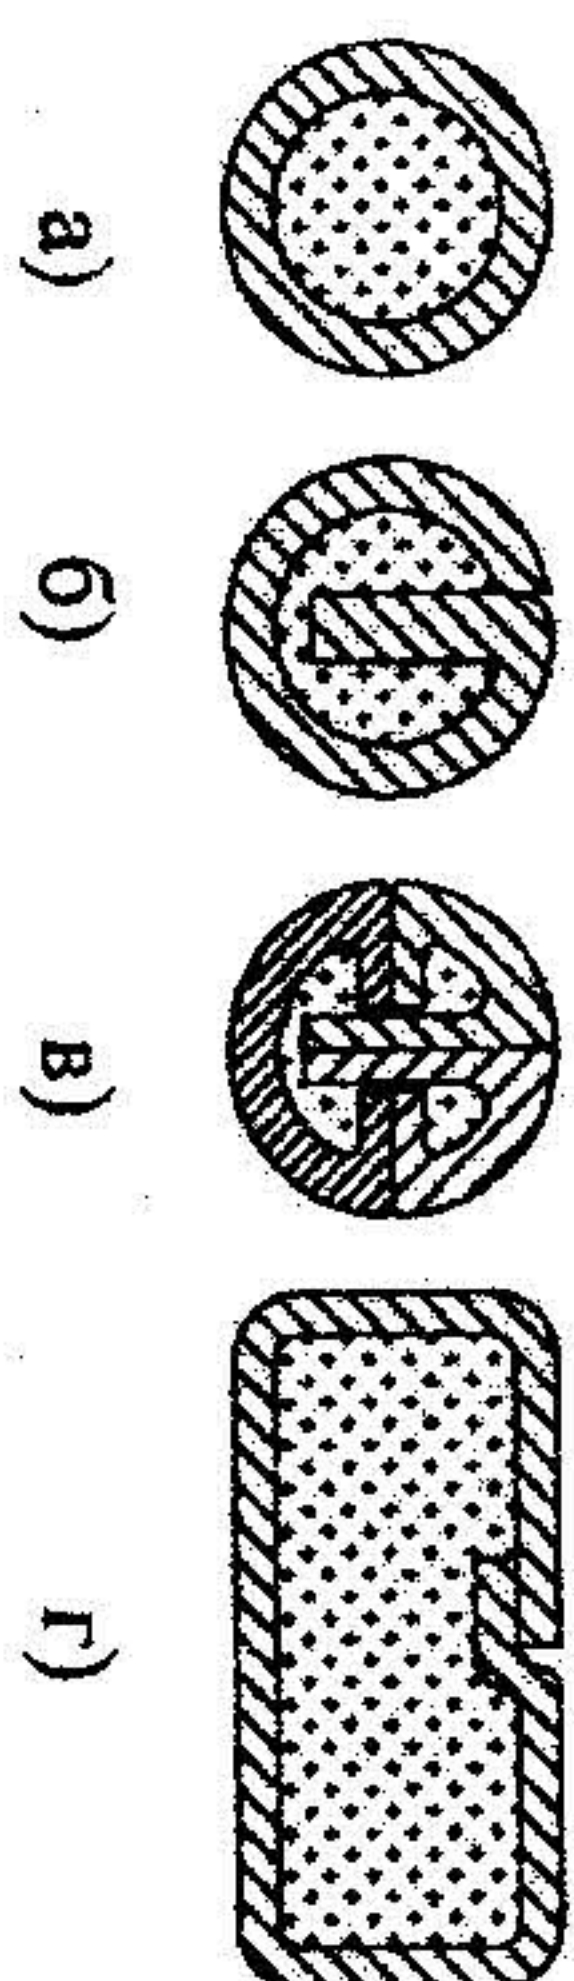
Основные конструкции порошковых проволок для наплавки:
